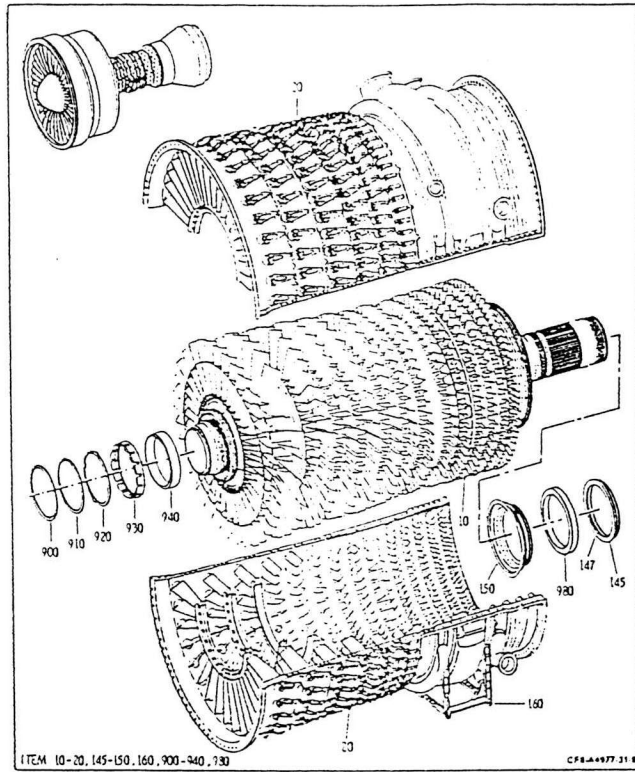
แสดงภาพ 2 A Module (Low Pressure Compressor Stator Assembly)
